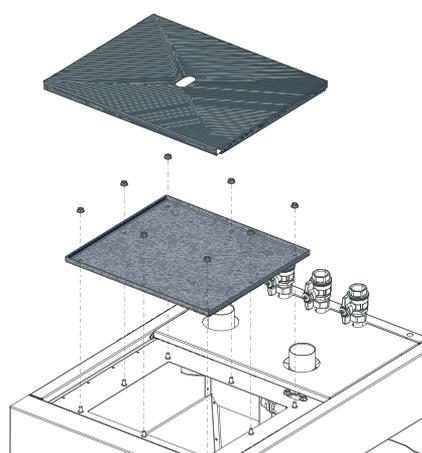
Retirer le cache avant, enlever les écrous, retirer le couvercle de révision
